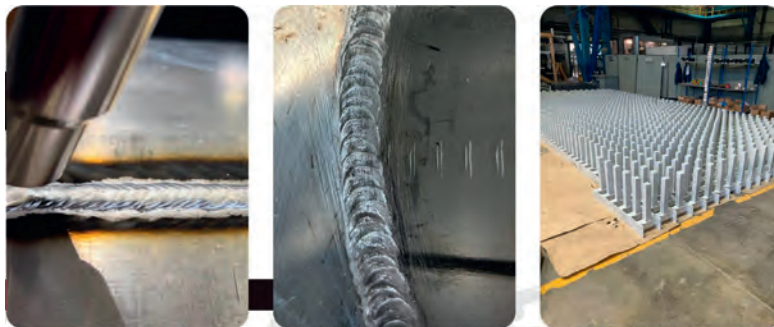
Сварной шов до и после зачистки, недельный объем, выполненный за один день. Фото: Technored
